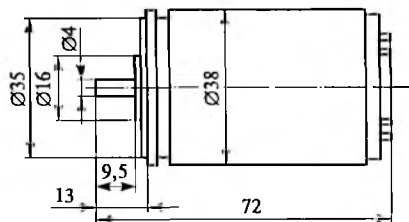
Габаритные и установочно-присоединительные размеры вращающегося трансформатора серии МВТ
